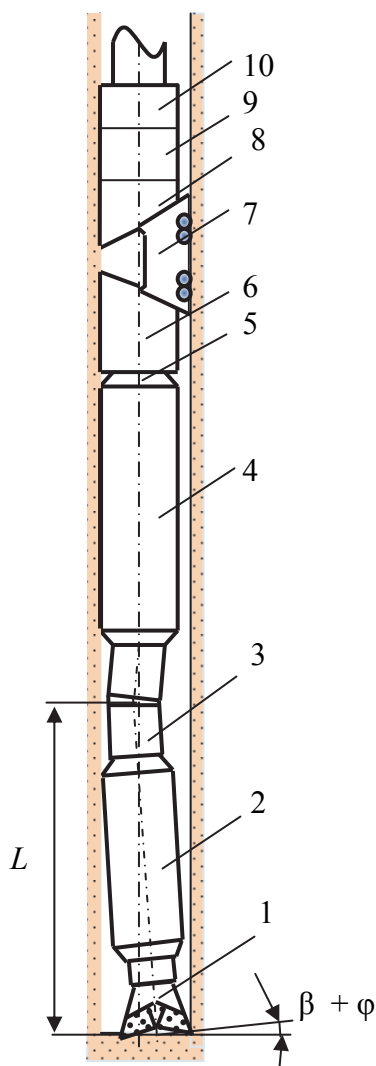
Отклонитель ОД-76: 1 – долото, 2 – шпindelь, 3 – шарнирное соединение и механизм регулирования угла перекоса, 4 – ВЗД, 5 – шарнирный вал, 6 – нижний полуклин, 7 – ползун с катками, 8 – верхний полуклин, 9 – гидропривод ползуна, 10 – переходник
